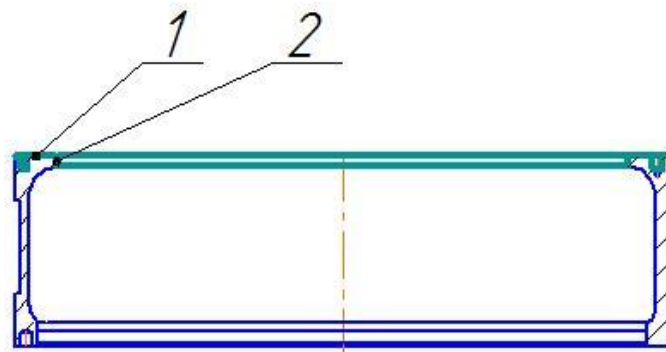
Контакт деталі з деталями у вузлі компресора в проточній частині
